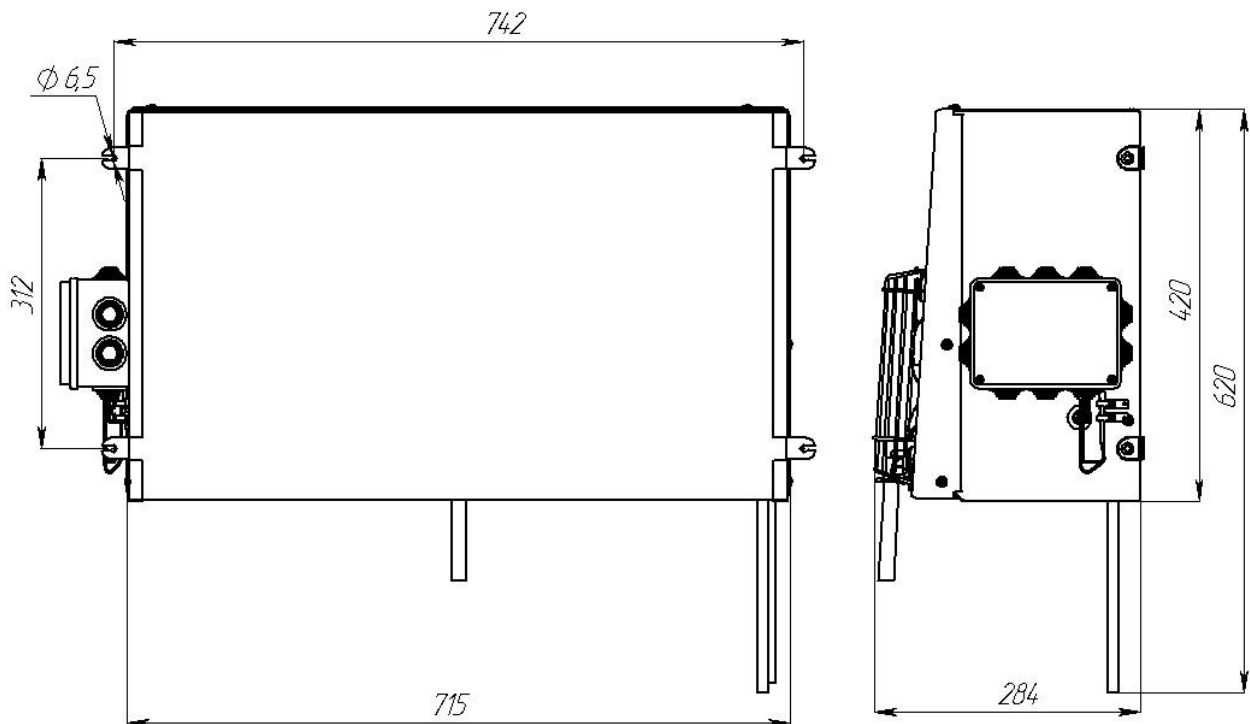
Габаритные и присоединительные размеры конденсаторного блока сплит-систем первого габарита
